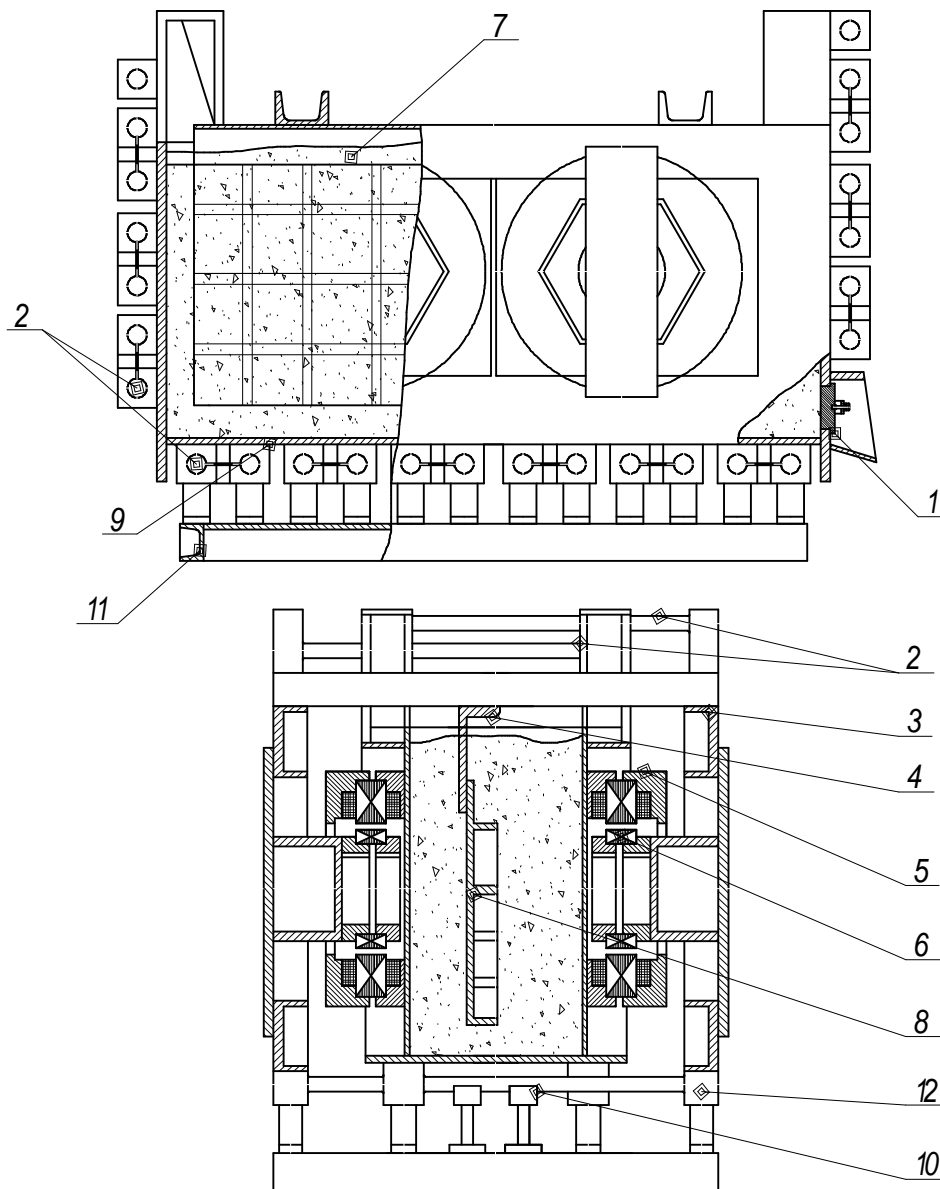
Конструктивна схема вібромашини для обробки плоских великогабаритних деталей
